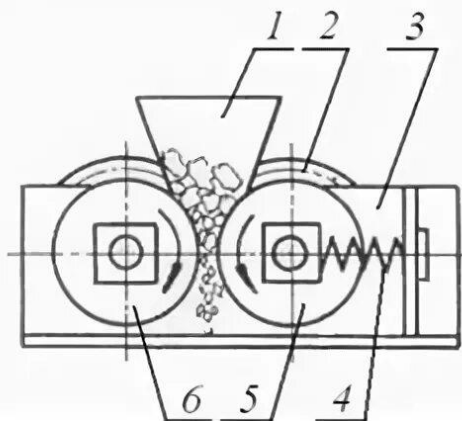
Дробилка вальцовая: 1 - бункер; 2 - привод; 3 - станина; 4 - пружина; 5, 6- валок
